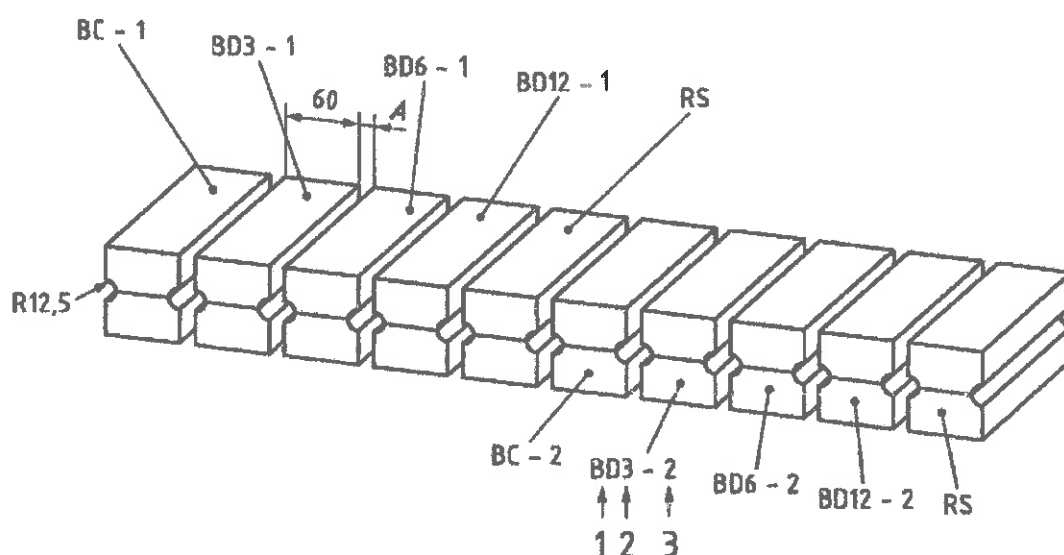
Plan de découpe d'un barreau d'essai et numérotation des éprouvettes
